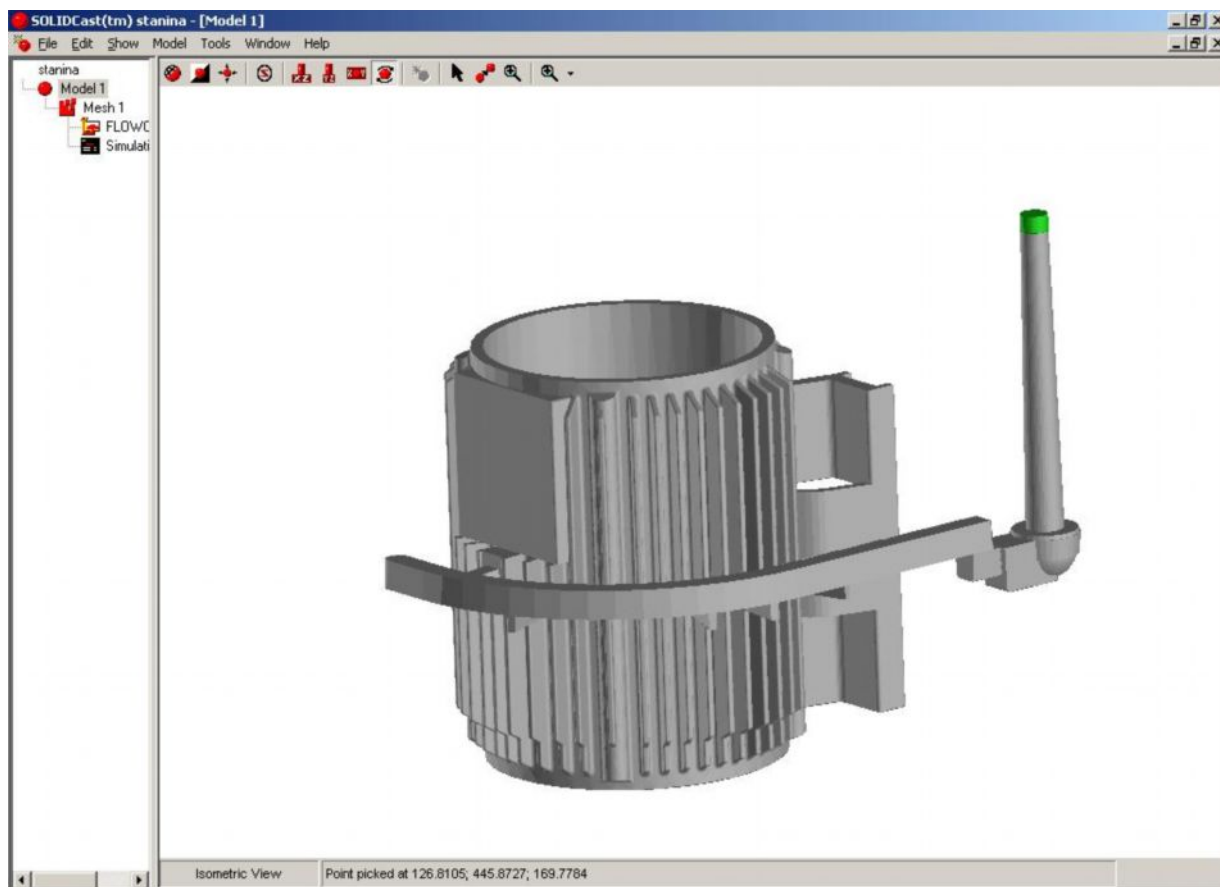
Общий вид отливки “Корпус электродвигателя”
